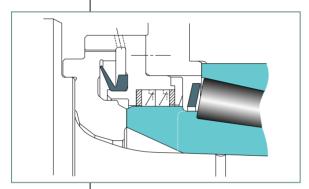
Assemblaggio di cuscinetto TQITSE
